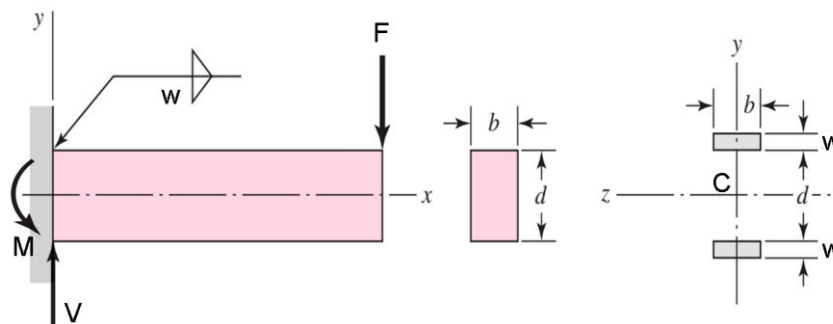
Conexión de un tubo a flexión con soldadura de filete.
